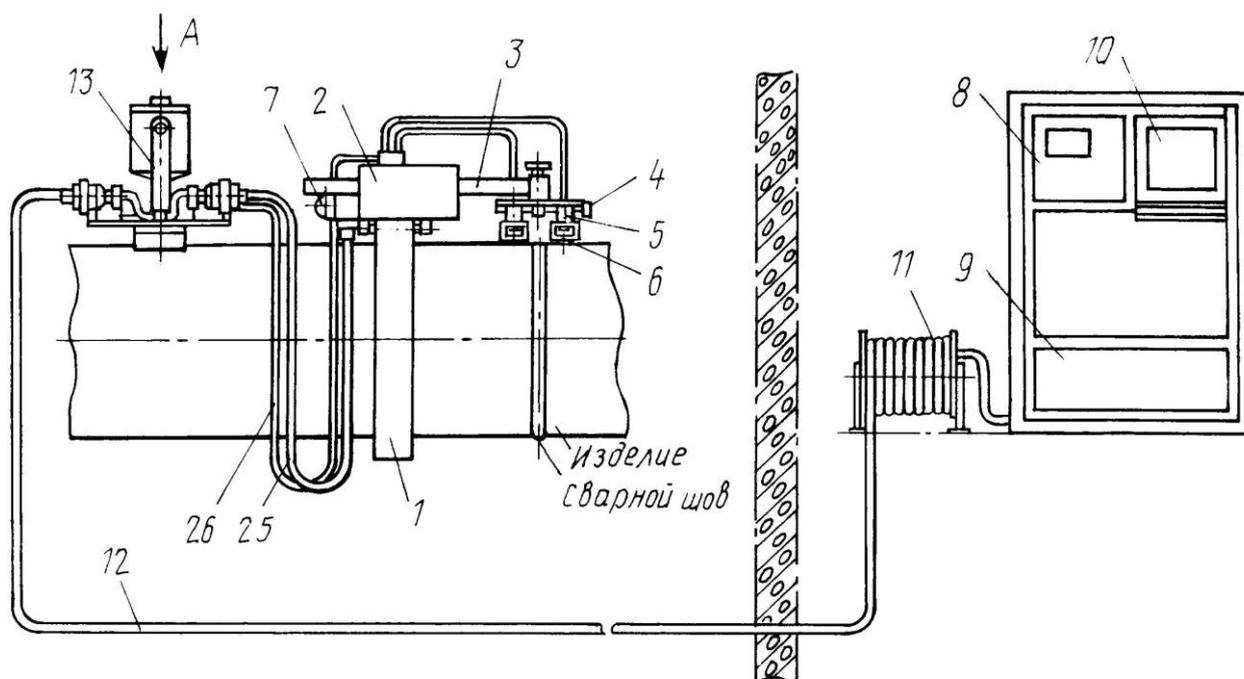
Устройство для АУЗК сварных кольцевых швов
